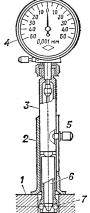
Шариковый индикаторный нутромер для измерения малых отверстий: 1— деталь; 2— упор; 3— измерительная вставка; 4— отсчётное устройство; 5— закрепительный винт; 6— игла; 7— измерительный шарик.
